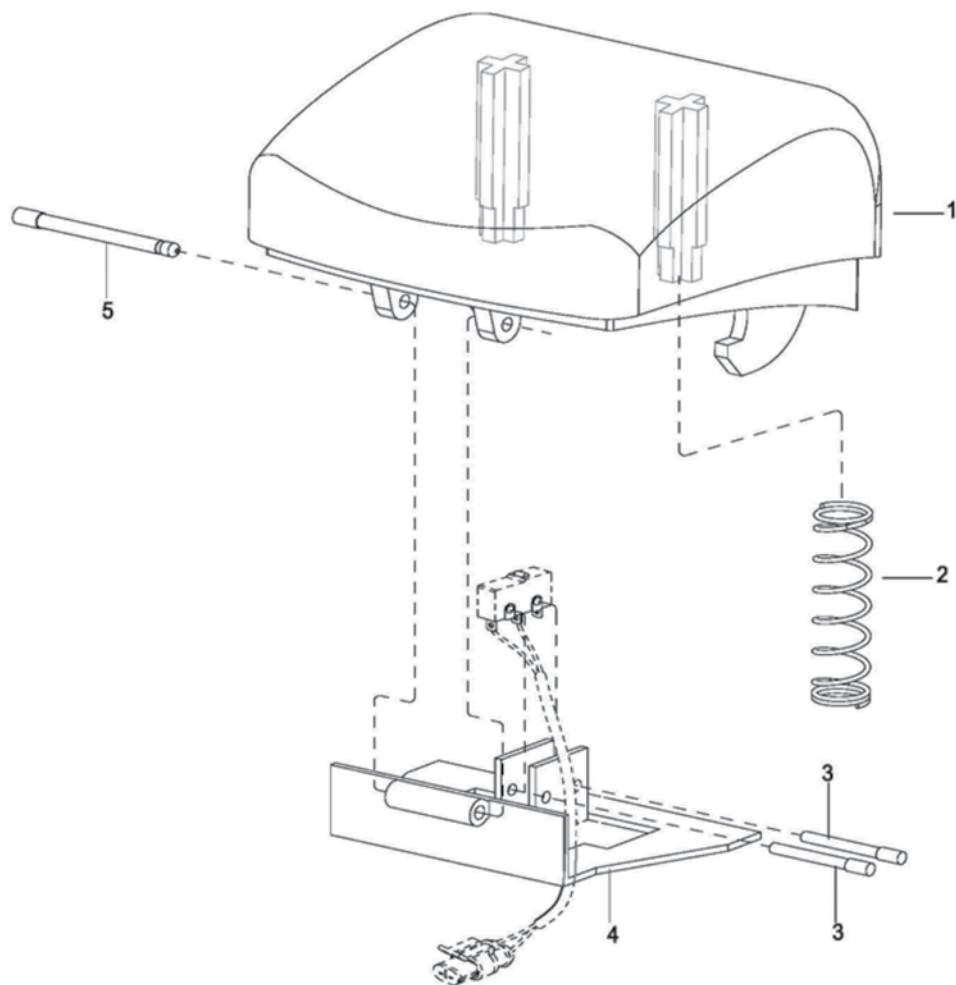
ASSEMBLAGE DU COUVERCLE
